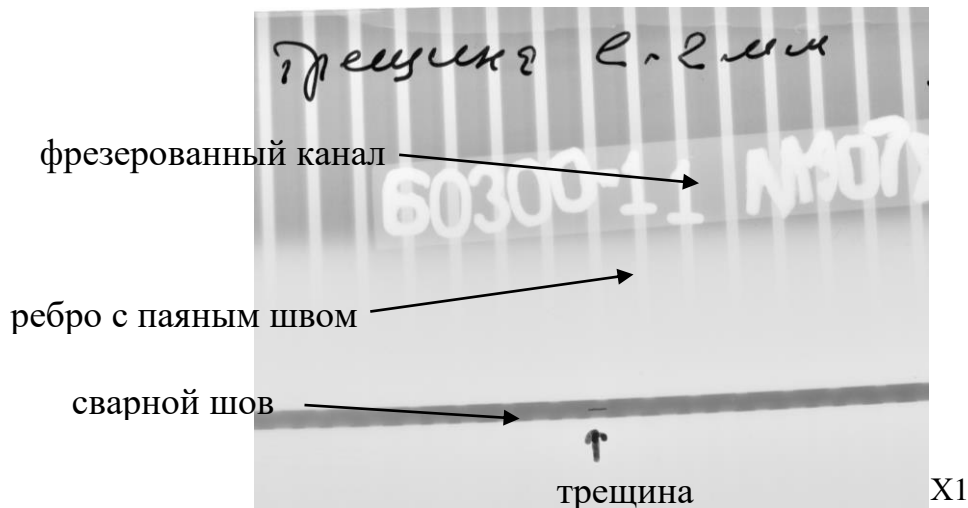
Рентгенограмма сварного шва стали 12X18H10T-ВД с трещинами
